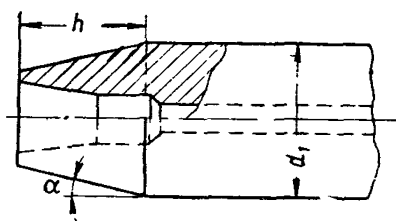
Размеры наружного конуса свечи измененной конструкции
